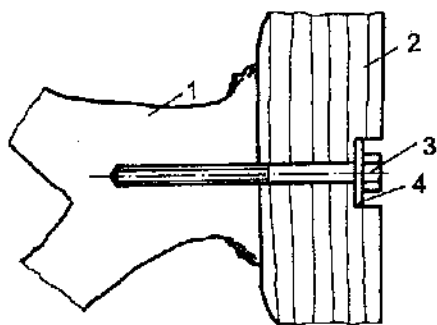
Крепление рога (1) к опорной доске (2); 3 — болт; 4 — шайба
